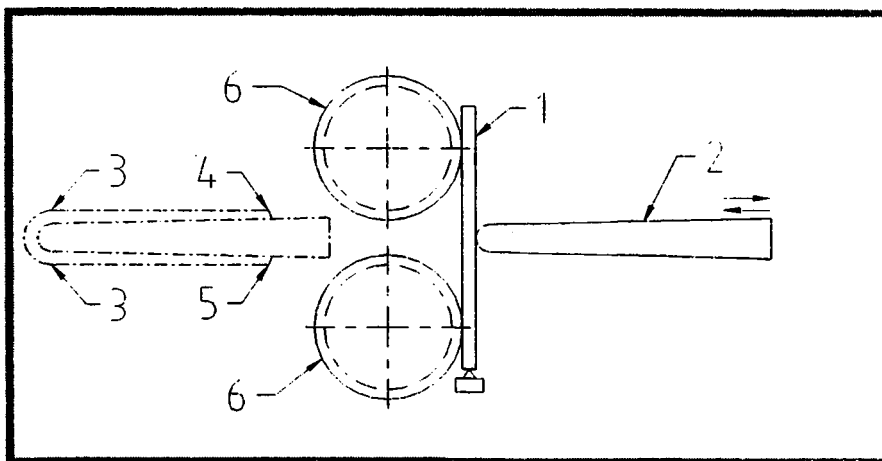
Схемы прокатки или вытяжки с изгибом заготовки [13]
